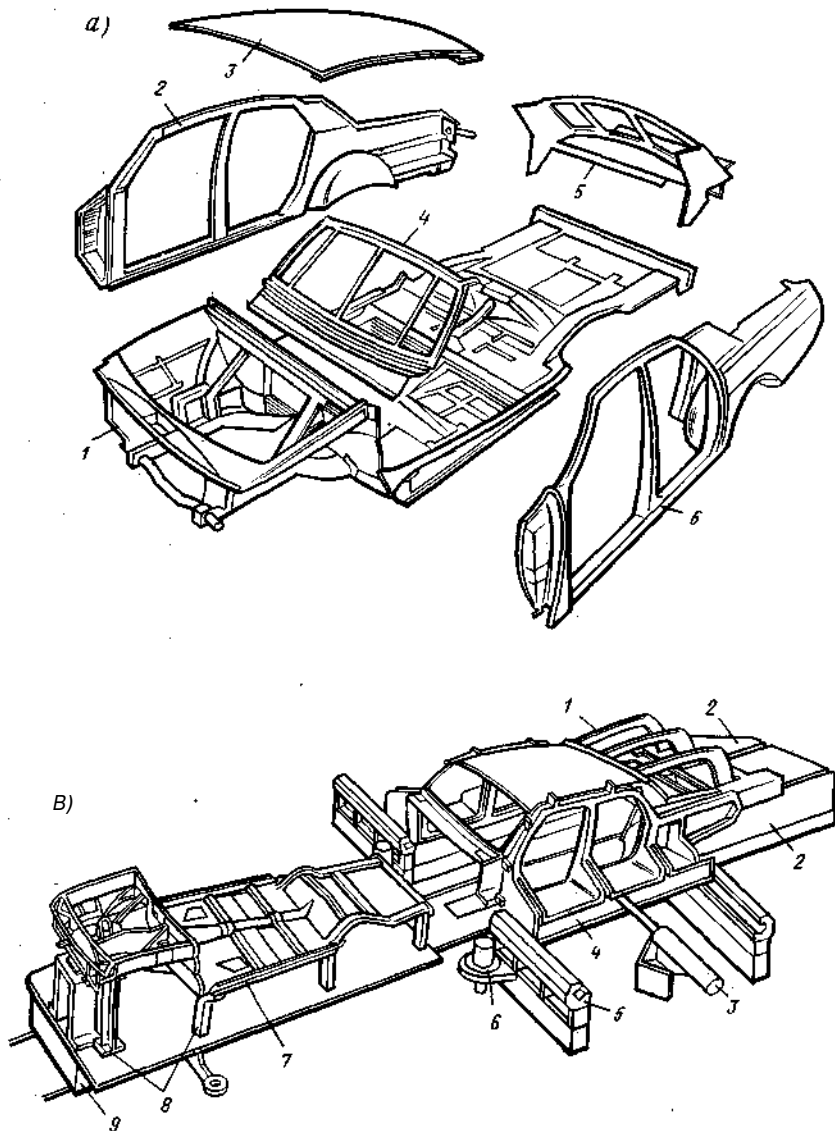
Сборка корпуса кузова легкового автомобиля ГАЗ-24:
